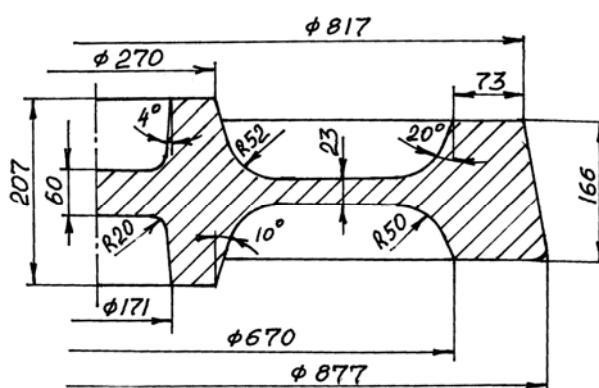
Размеры колесной заготовки формовочного пресса усилием 100 МН для колес диаметром 957 мм
